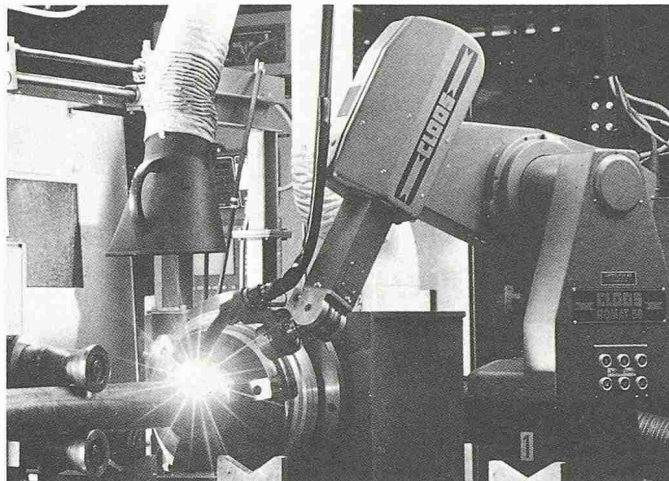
CNC-gesteuerter Schweißroboter der Firma Cloos zum Anschweißen der Walzenböden
